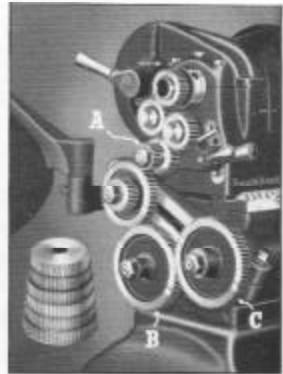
Torno com engrenagens standard de mudança, visto do extremo.
